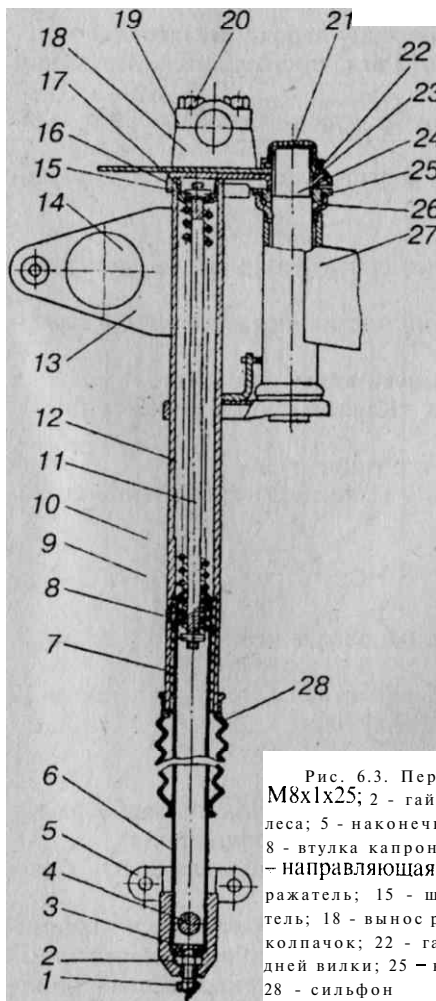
Передняя вилка мокика "Карпаты": 1 - болт М8х1х25; 2 - гайка М8х1; 3 - шайба; 4 - ось переднего колеса; 5 - наконечник штока; 6 - шток; 7 - втулка распорная; 8 - втулка капроновая; 9 - пружина отбоя; 10 - пружина; 11 - направляющая; 12 - остов; 13 - кронштейн фары; 14 - отражатель; 15 - штифт; 16 - траверса верхняя; 17 - держатель; 18 - вынос руля; 19 - крышка; 20 - болт М8х1х25; 21 - колпачок; 22 - гайка; 23 - кронштейн; 24 - стержень передней вилки; 25 - конус верхний; 26 - подшипник; 27 - рама; 28 - сильфон
